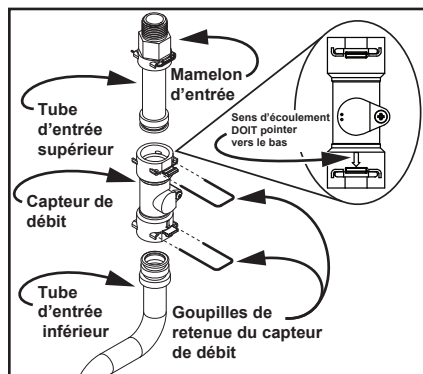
Démontage des composants d'entrée et dépose du capteur de débit.
